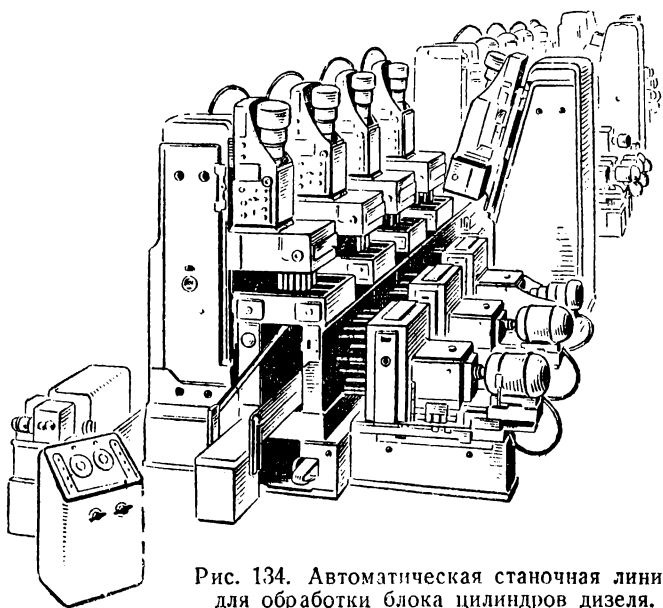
Автоматическая станочная линия для обработки блока цилиндров дизеля.
